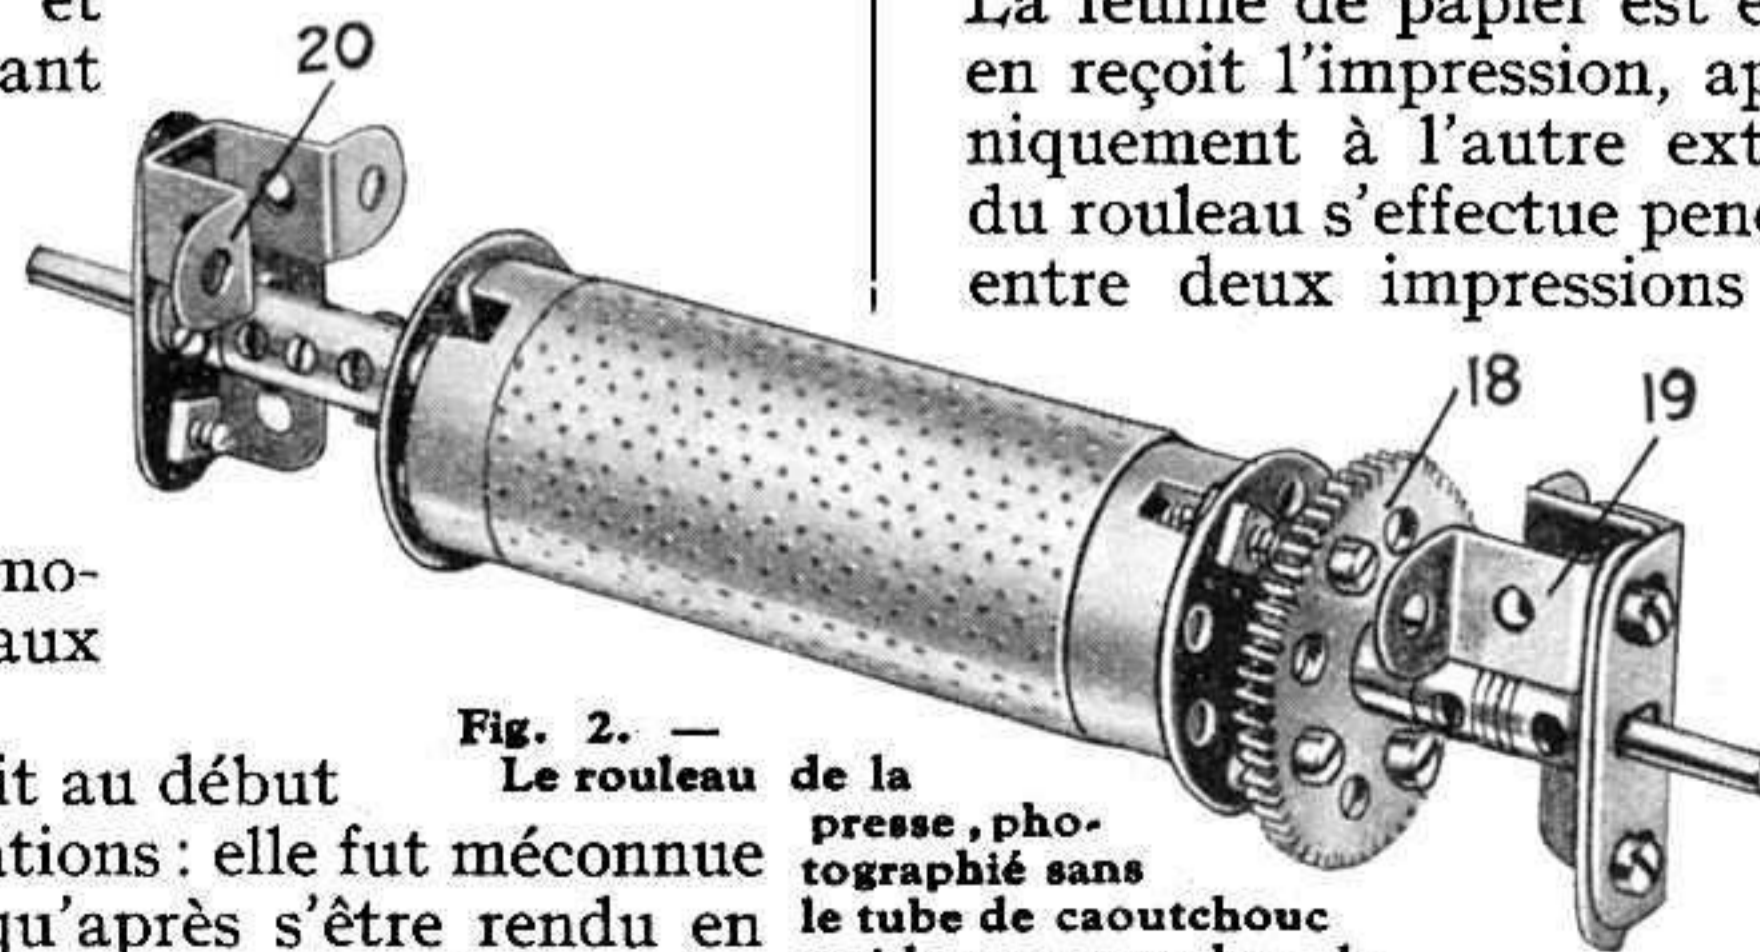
Le rouleau de la presse, photographié sans le tube de caoutchouc qui le recouvre lors de l'impression.
